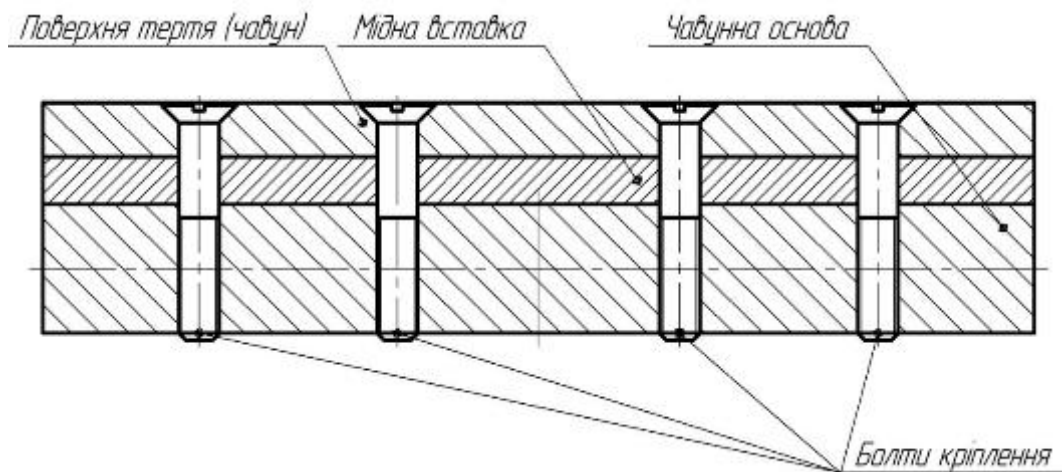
Конструкція експериментального диска з біметалічним поверхневим шаром;
